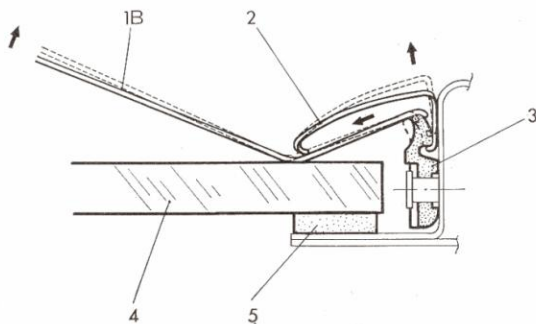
Demonstration der Anwendung der Werkzeuge A. 78032.
